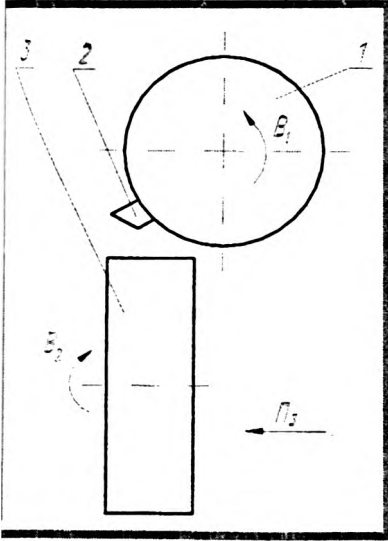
Кинематическая схема обработки пазов на цилиндрической заготовке
